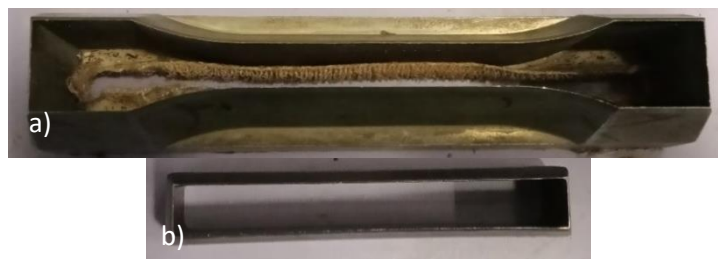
Emporte-pièce : a) Pour les éprouvettes de type 1B. b) pour les éprouvettes de flexion.
